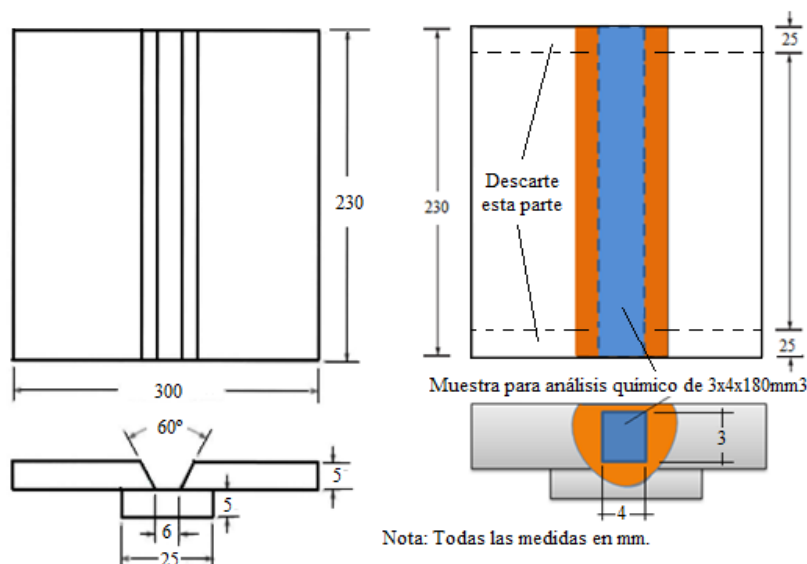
Diseño de junta para prueba de análisis químico en depósito de soldadura en la junta soldada AA5083-H116. Adaptado de [26].
